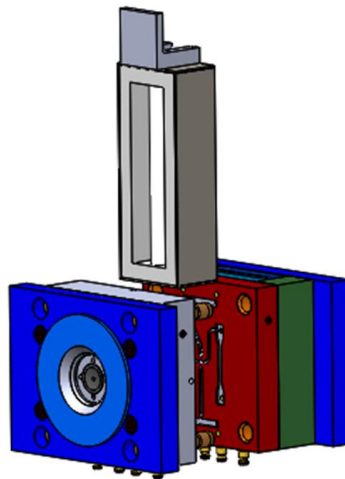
Desenho CAD do suporte de lâmpadas e molde projetados.
